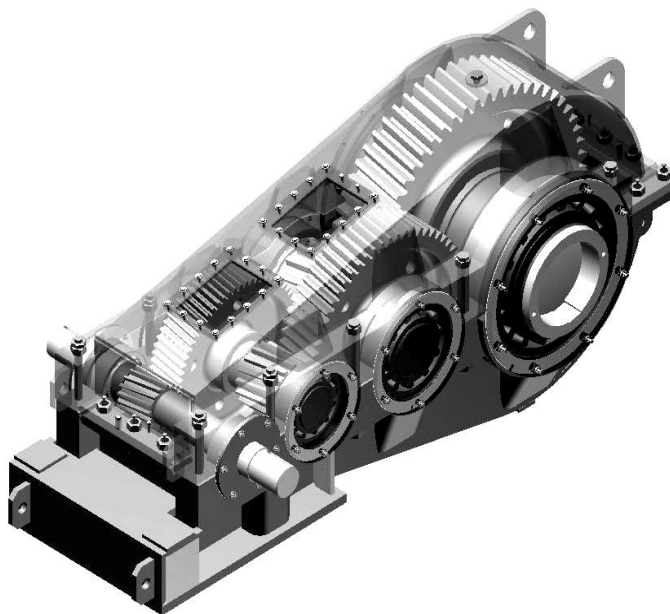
Приклад застосування корпусної деталі в конструкції редуктора
